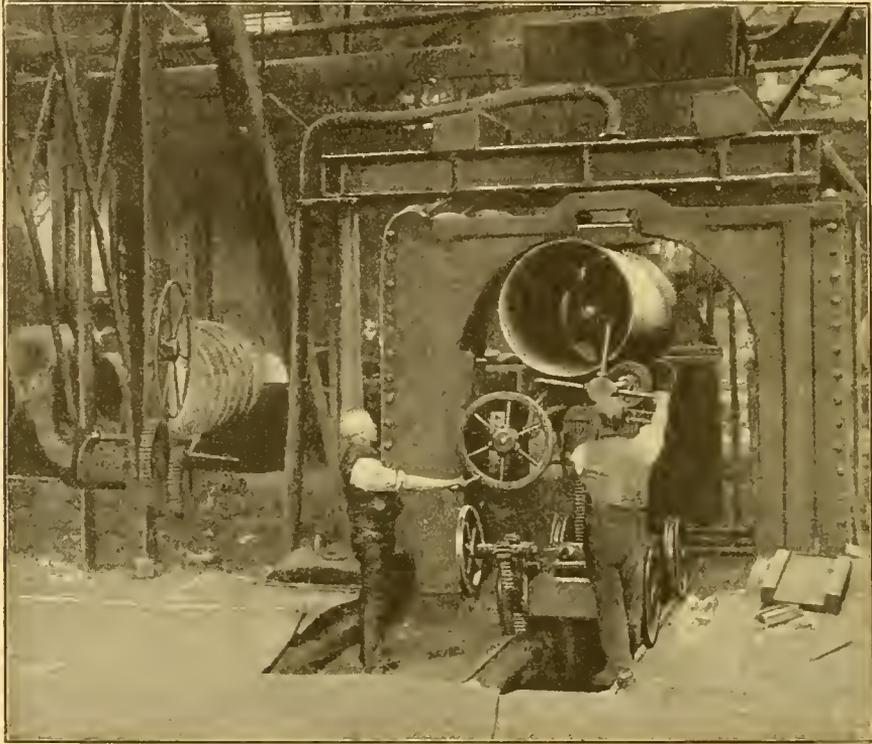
Appareil pour le soudage par le gaz à l'eau, pouvant convenir à la fabrication des tubes depuis 250 millimètres jusqu'à 2^m,500 de diamètre.
